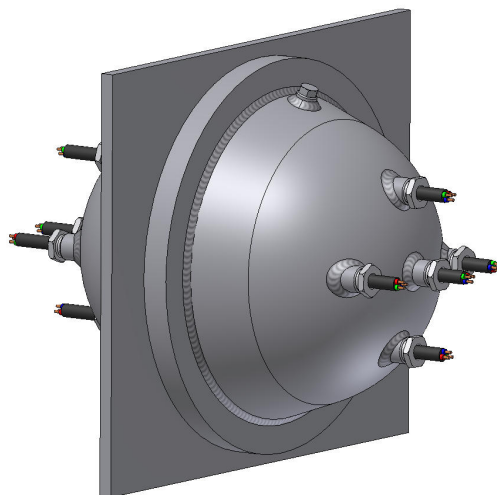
Трёхмерная модель конструкции опытного образца уплотнительного устройства
